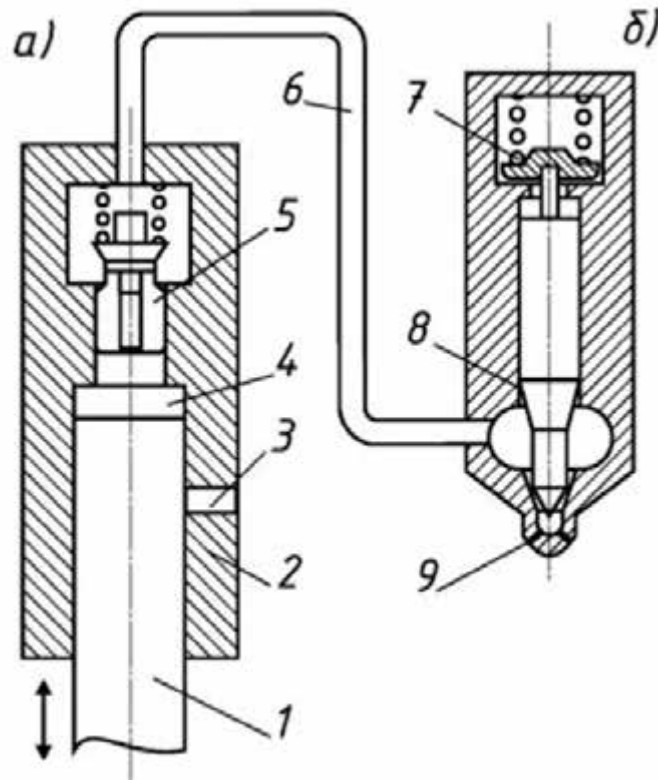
Схема паливної системи дизельного двигуна: 1 – плунжер, 2 – втулка плунжера, 3 – наповнювальний отвір, 4 – надплунжерний простір, 5 – зворотний (нагнітальний) клапан, 6 – паливопровід високого тиску, 7 – пружина голки форсунки, голка форсунки, 9 – сопловий наконечник
